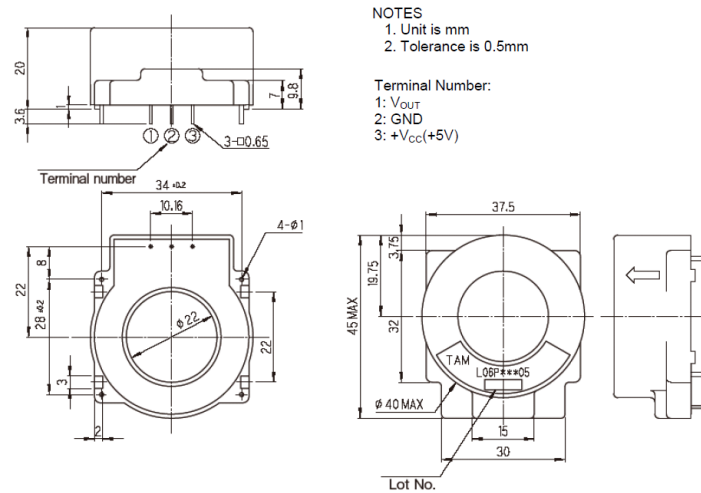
Desenho técnico do sensor de corrente L06P800S05 (Tamura Corporation, 2012)
